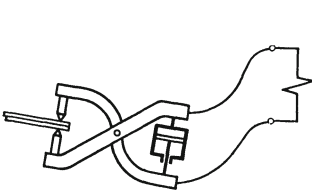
Schweißzange mit Preßluftbetrieb.
